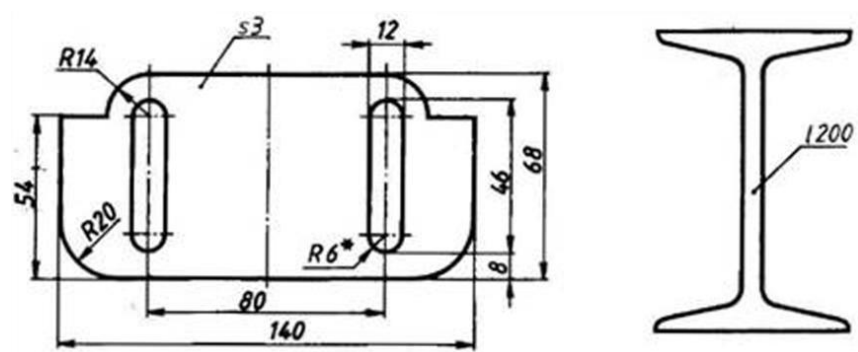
Чертежи плоских деталей с обозначением толщины и длины
